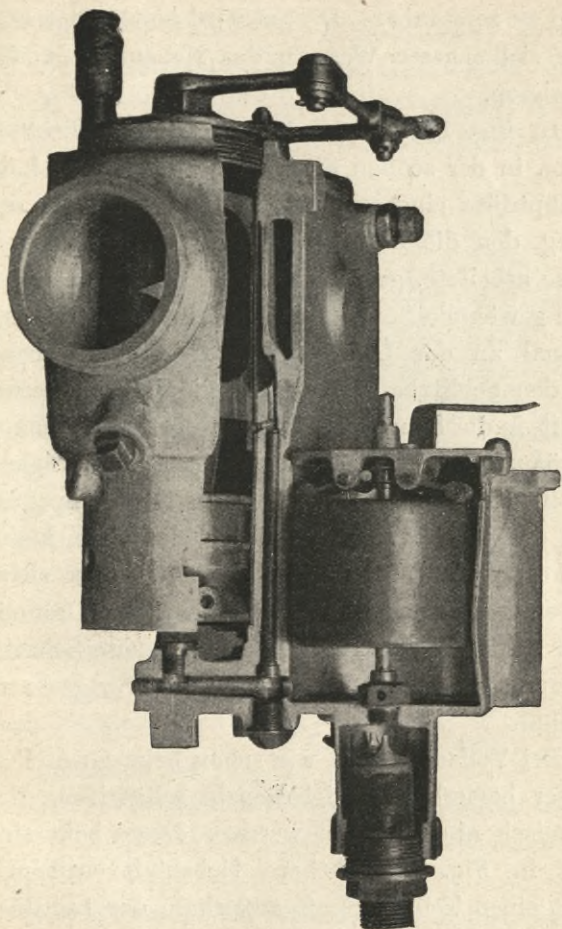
Mercedes-Vergaser zum Teil aufgeschnitten.
